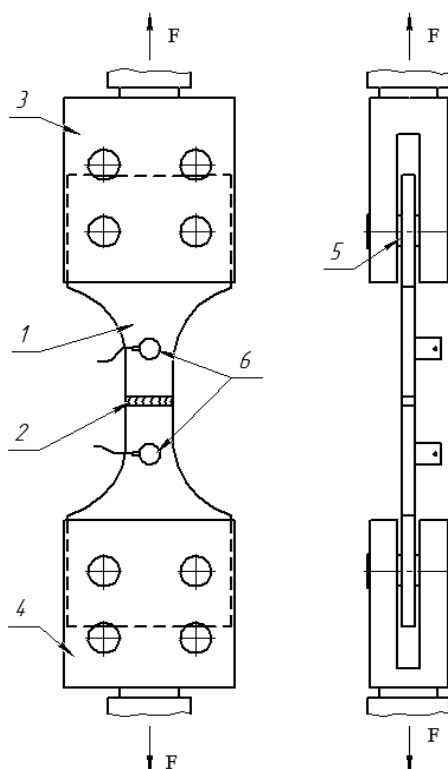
Схема нагружения образца: 1 – образец; 2 – сварной шов; 3 – верхний захват нагружающего устройства; 4 – нижний захват нагружающего устройства; 5 – палец; 6 – ПАЭ
